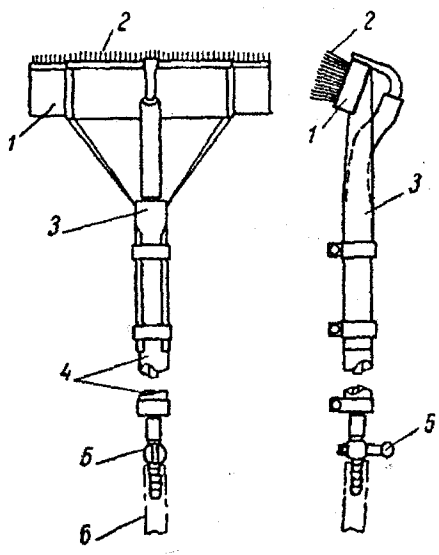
Механізована щітка для очищення фасаду методом промивання
